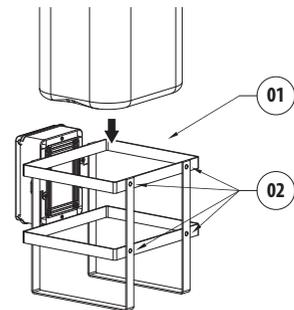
Réservoir 23l, hauteur de remontée de 5m ou 11m.
